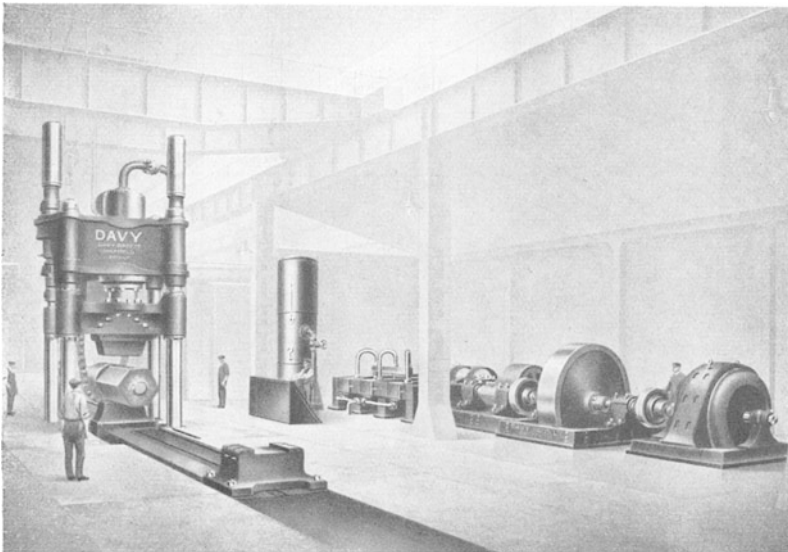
Pumpenanlage für direkten Betrieb einer 1500 t-Schmiedepresse.
